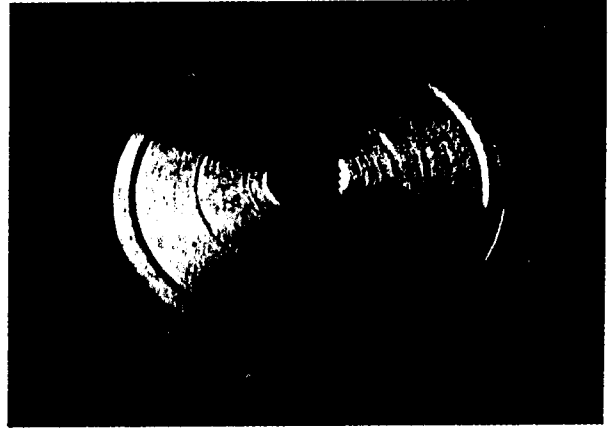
焊头端表面(与变幅杆相接处)的划伤形貌
